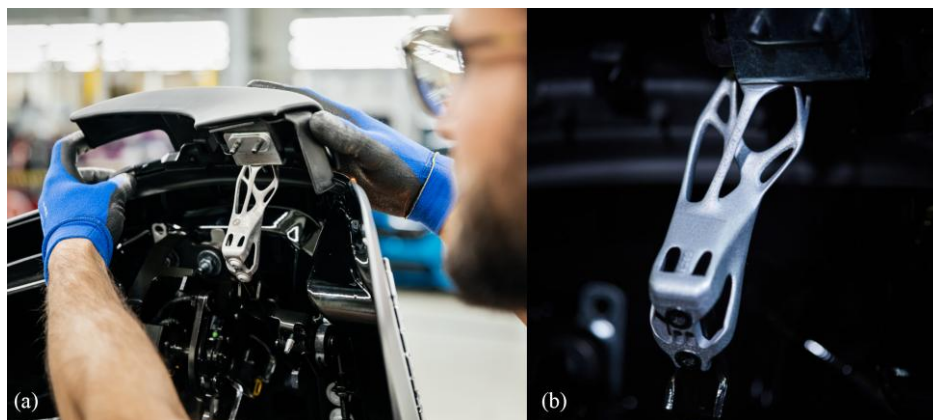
Fixação de capota fabricada pela BMW: Montagem do componente (a); Imagem em detalhe da fixação (b) [8, 9].
